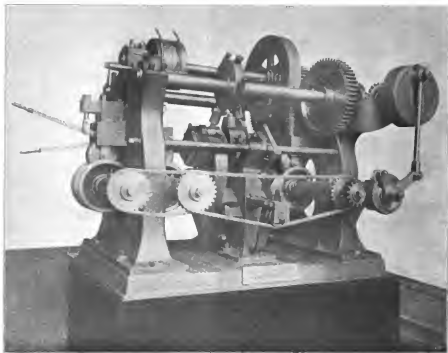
Patent-Winkeisen-Abgratmaschine.
